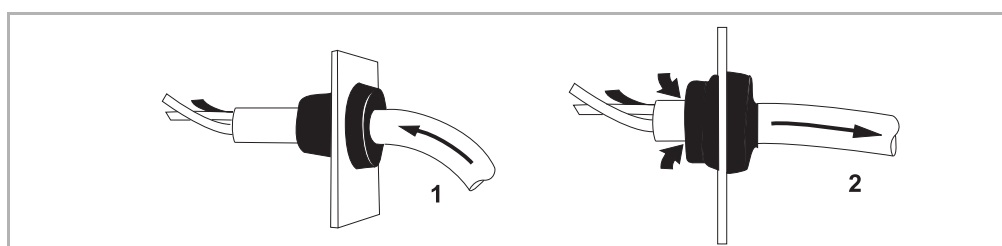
Drahtmontage - Kabelverschraubungen
